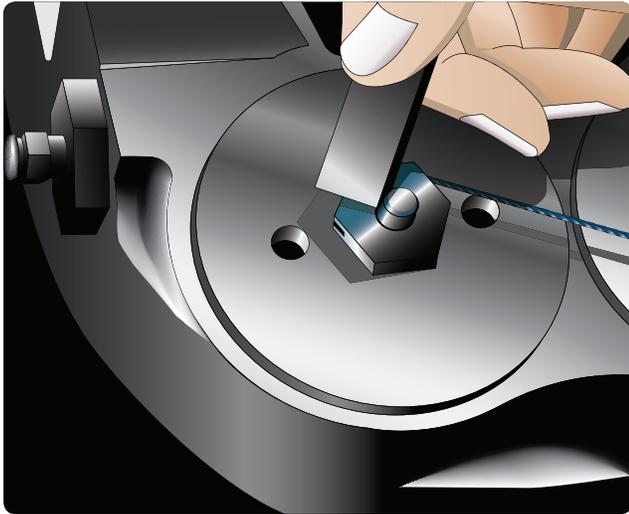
Desgaste das pastilhas de freio em um freio Goodyear é determinado medindo o pino de desgaste do ajustador automático.
